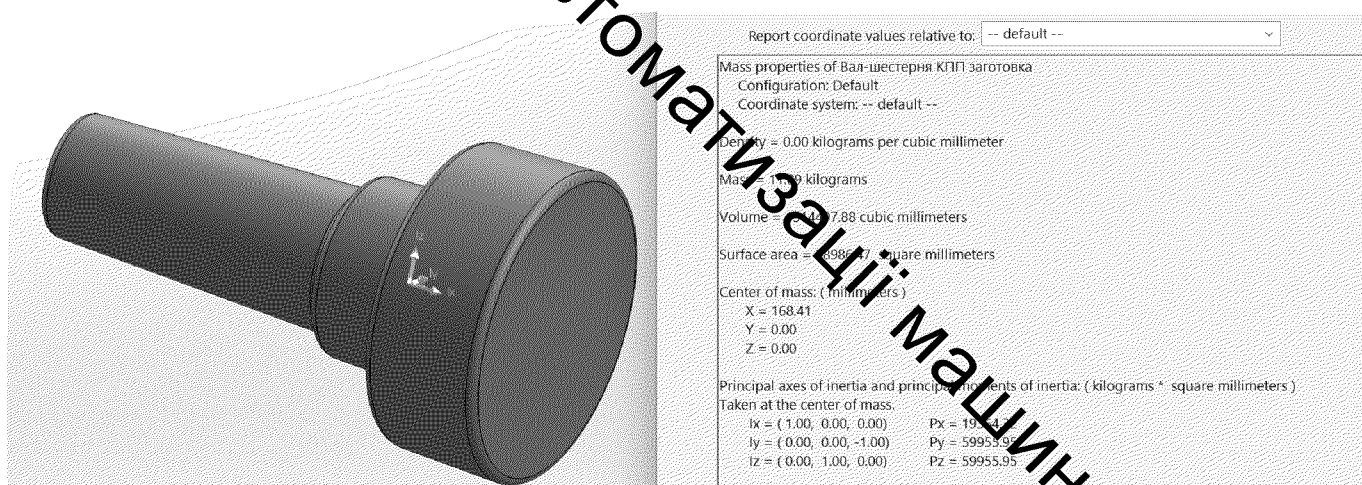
3-D модель заготовки в «Solidworks»
